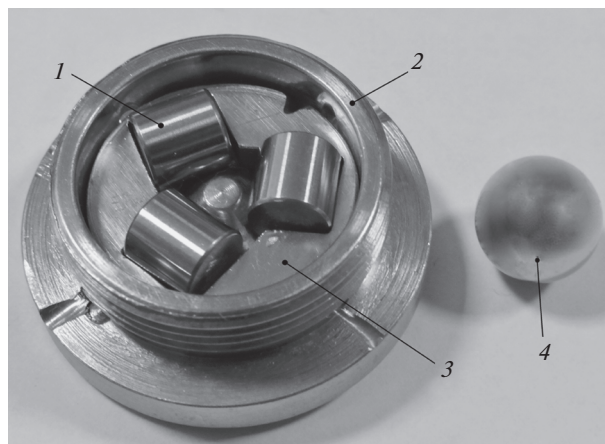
Оправка в сборе (крышка снята): 1 — ролик; 2 — корпус оправки; 3 — сепаратор; 4 — верхний шарик.
